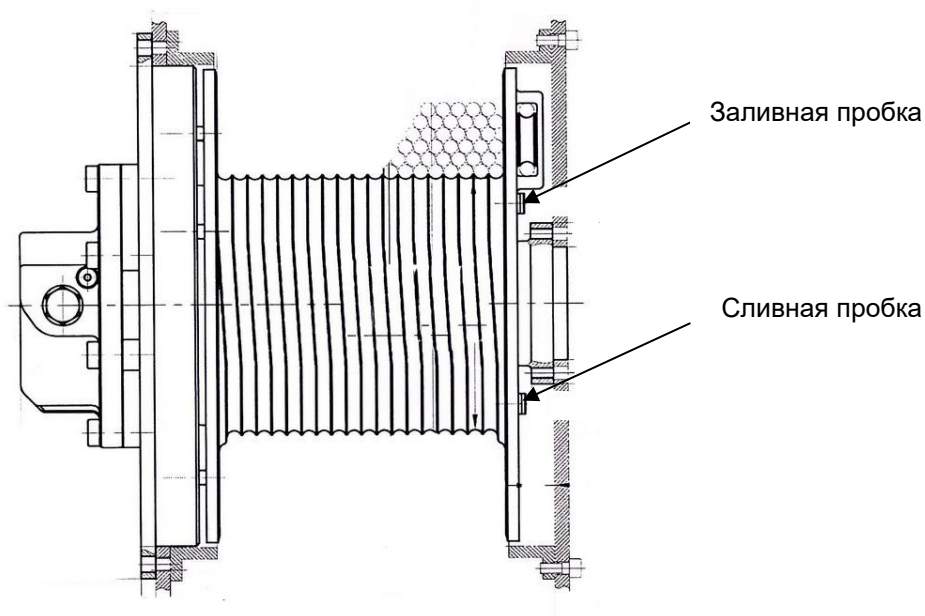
Лебедка с расположением сливной и заливной пробок на боковой (торцевой) поверхности барабана
